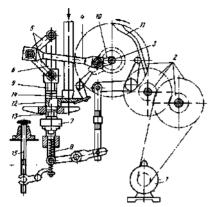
Кинематическая схема коленорычажного пресса СМ-143: 1 - электродвигатель; 2 - шестерни привода; 3 - коленчатый вал; 4 - шатун; 5 - серьга; 6 - штанга; 7 - траверса; 8 - пружины; 9 - верхние пуансоны; 10 - кулак привода каретки; 11 - кулак привода механизма выталкивания; 12 - засыпная каретка; 13 - нижние пуансоны; 14 - засыпной ящик; 15 - механизм регулирования высоты засыпки массы в пресс-форму
